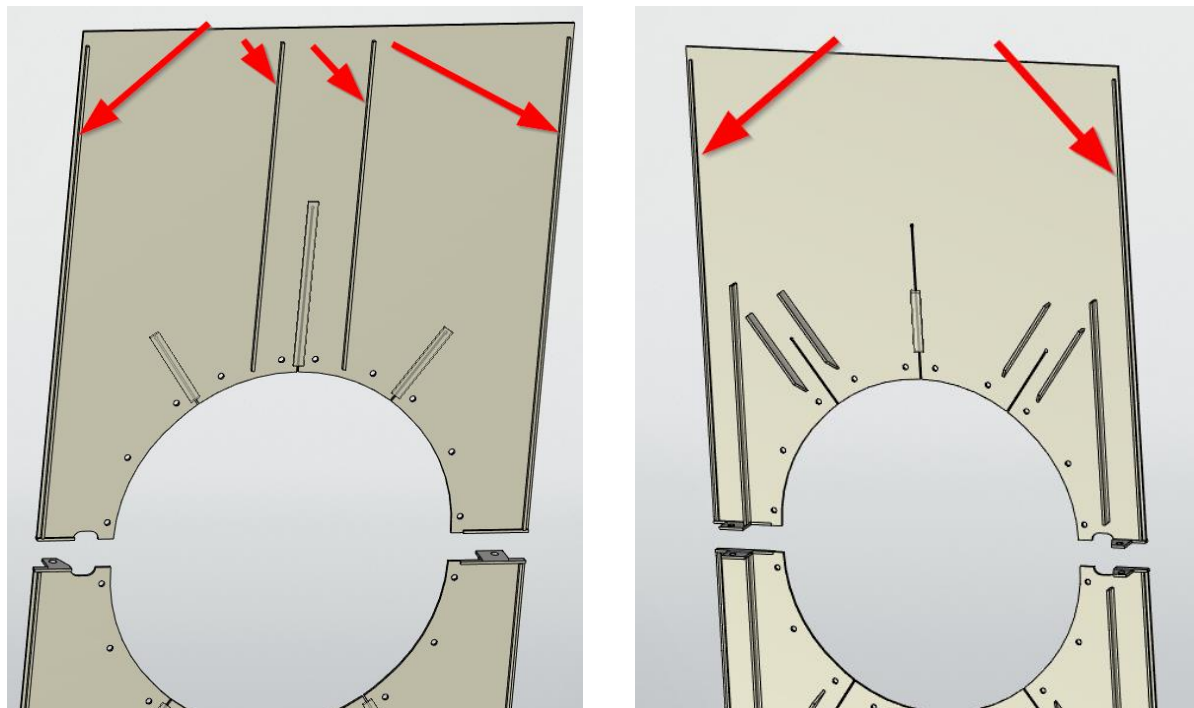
Приварка полосок для уменьшения поверхности контакта щита с каркасом (слева вид со стороны топки, справа – вид со стороны цеха)
